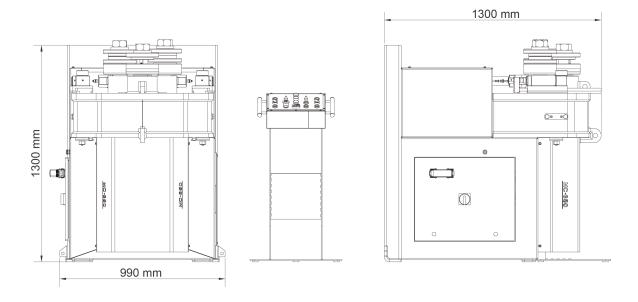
Dimensiones de la máquina con la bancada en posición horizontal
